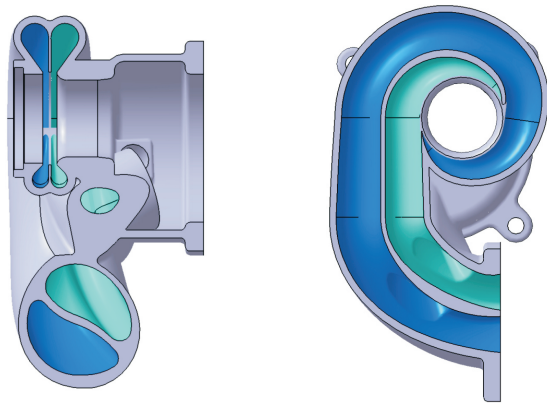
Zweiflutige Turbinengehäuse. Links ist eine Zwillingsstromturbine und rechts eine Doppelstromturbine abgebildet.
